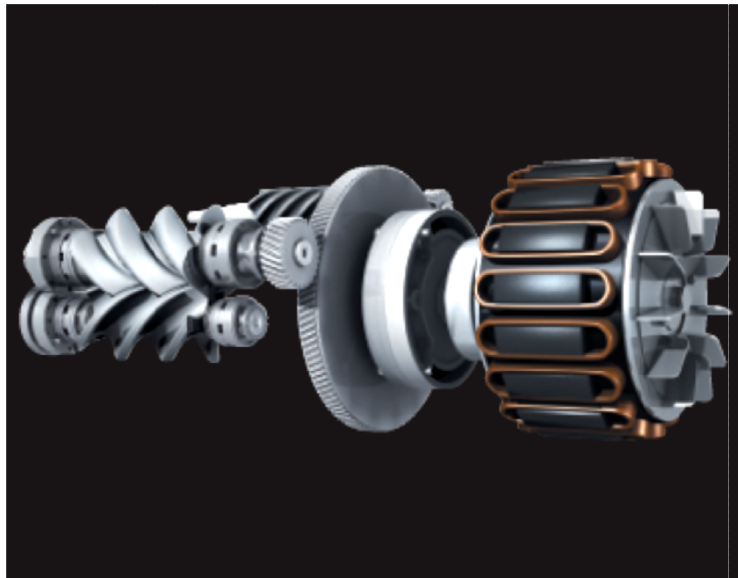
Rotores, e carretos da bull gear box com o motor (Fonte: *Ingersoll-Rand*)
